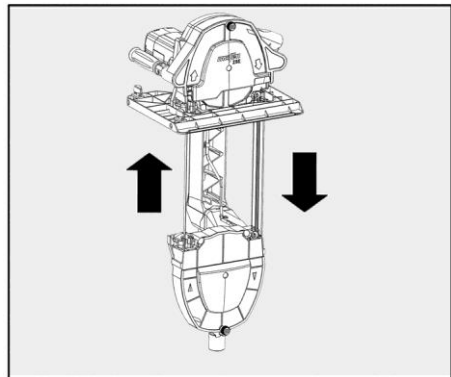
Dirección de giro del rodillo de sierra sin fin
